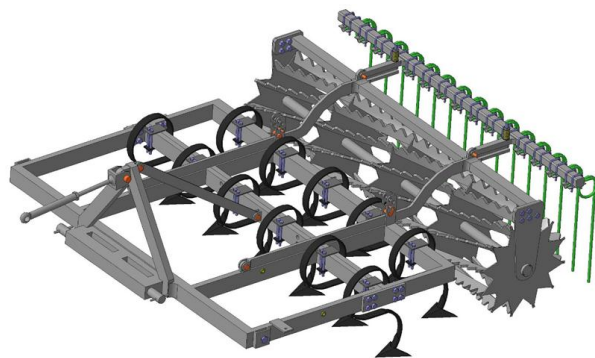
3D модель почвообрабатывающего агрегата
